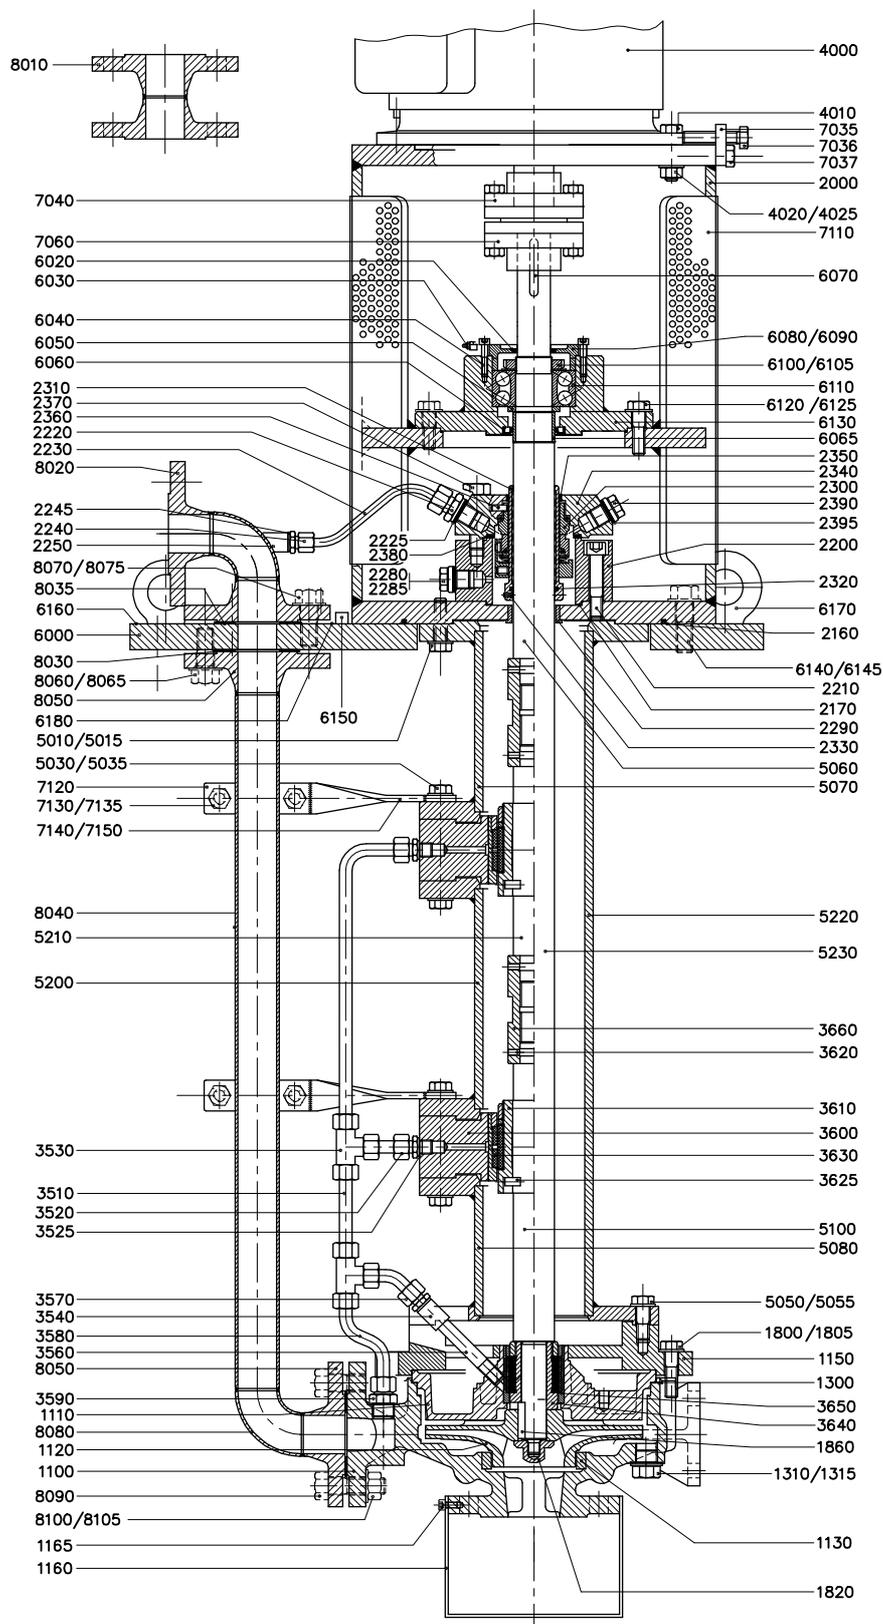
Pompe avec groupe d'étanchéité d'arbre M2.
